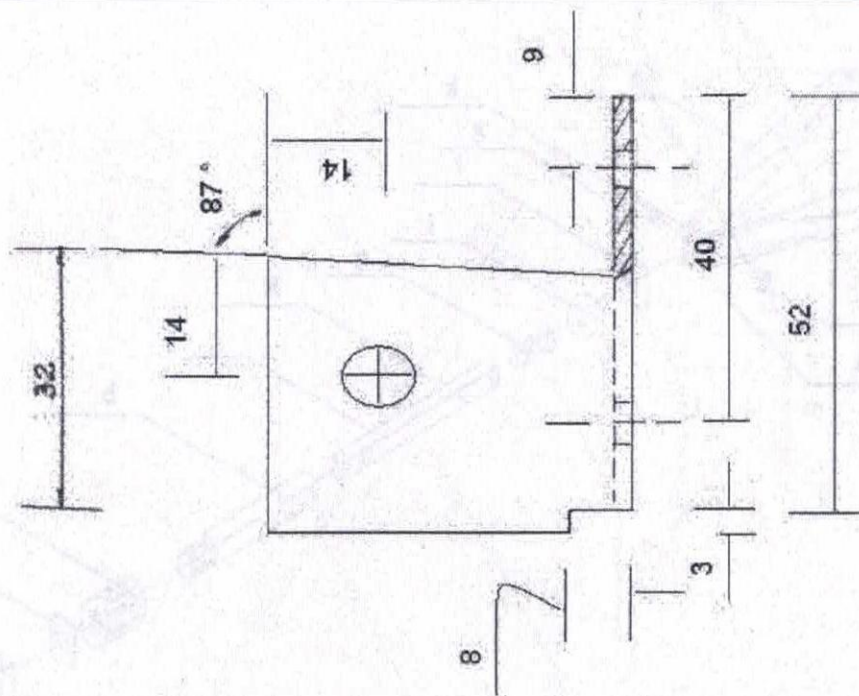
Vista de perfil do garfo de fixação da pá (medidas em mm)
